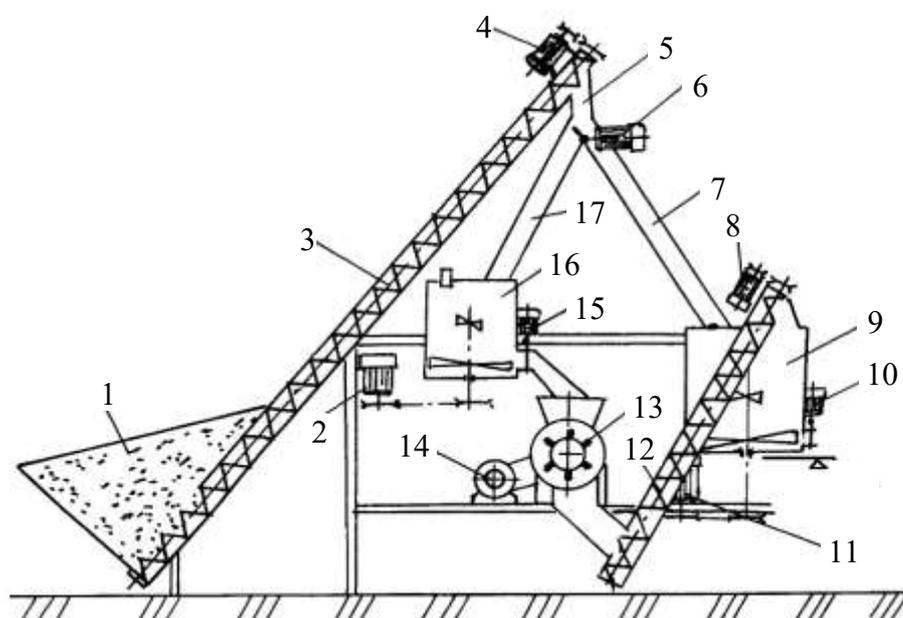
Конструктивная схема агрегата приготовления премиксов АП-100:
